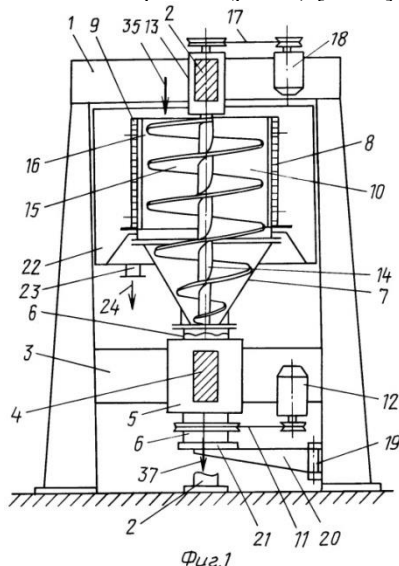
Фильтрующая центрифуга для обезвоживания сапропеля [15]
